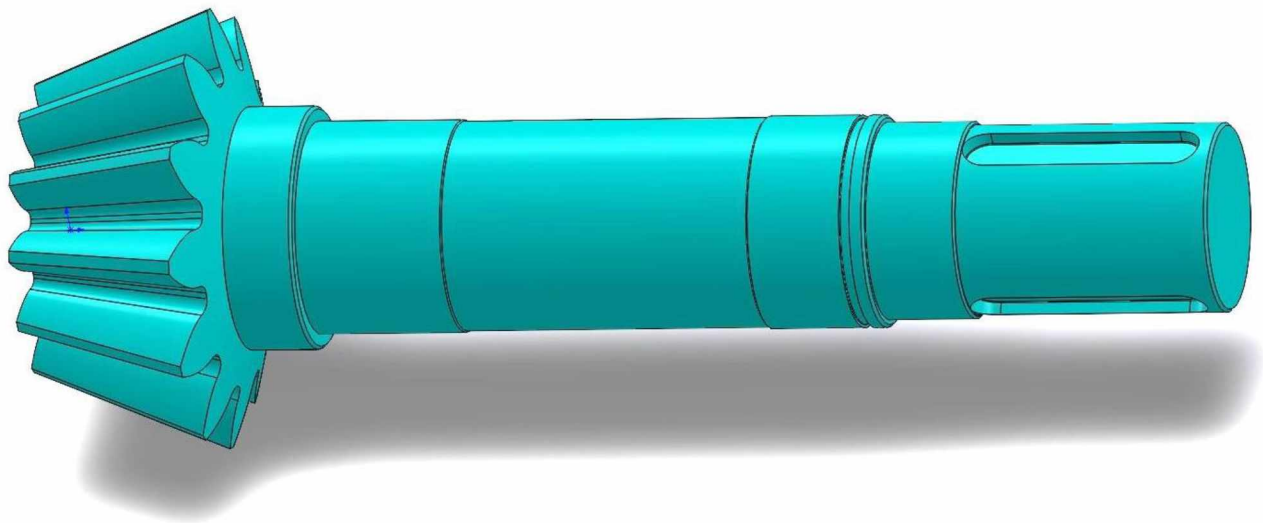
3D модель деталі «Вал-шестерня»
